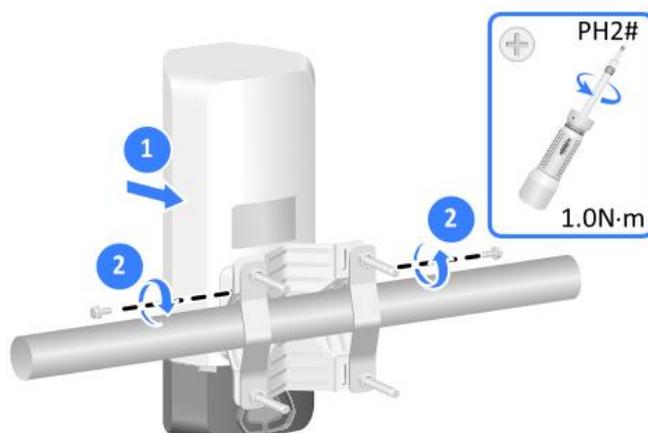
Asegure el Dispositivo al Soporte de Montaje
